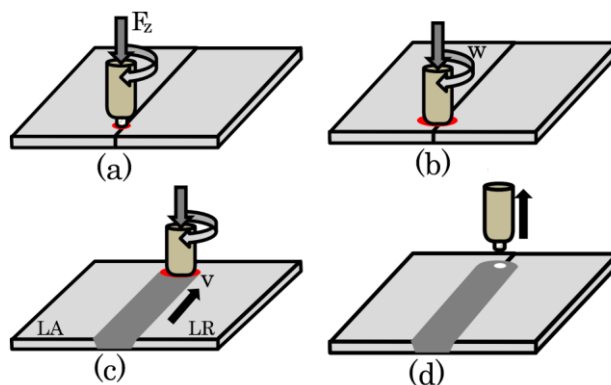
Representação esquemática do processo: (a) aproximação da ferramenta; (b) penetração da ferramenta entre as faces das chapas até à estabilização; (c) soldadura; (d) fim da soldadura e remoção da ferramenta [37].
